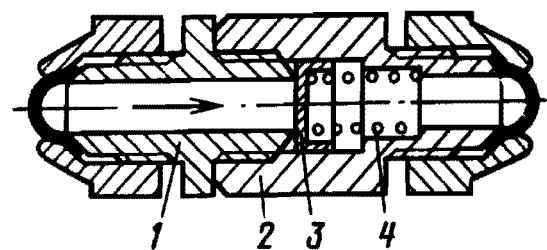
Обратный клапан с подсоединением под отбортовку для малого диаметра прохода:
